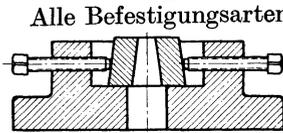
Froschplatte für austauschbare Schnittplatten.
